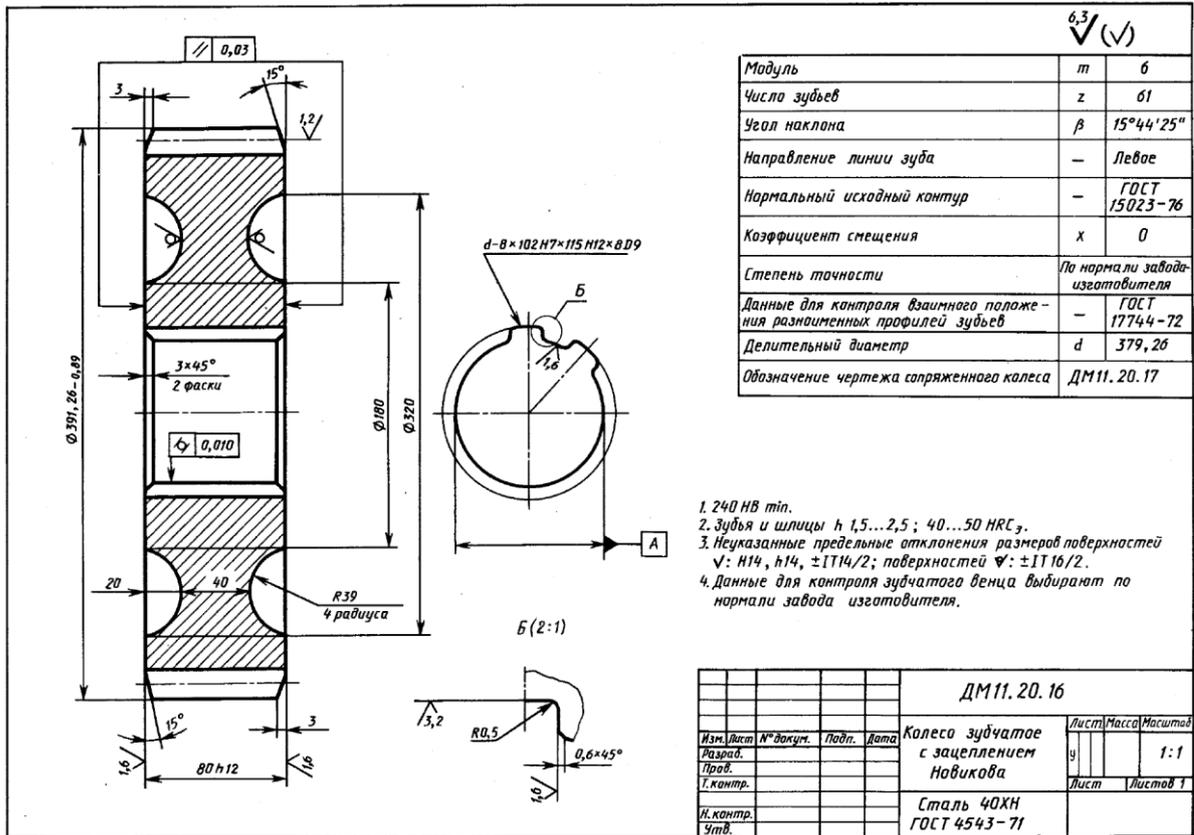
Рабочий чертеж зубчатого цилиндрического колеса
